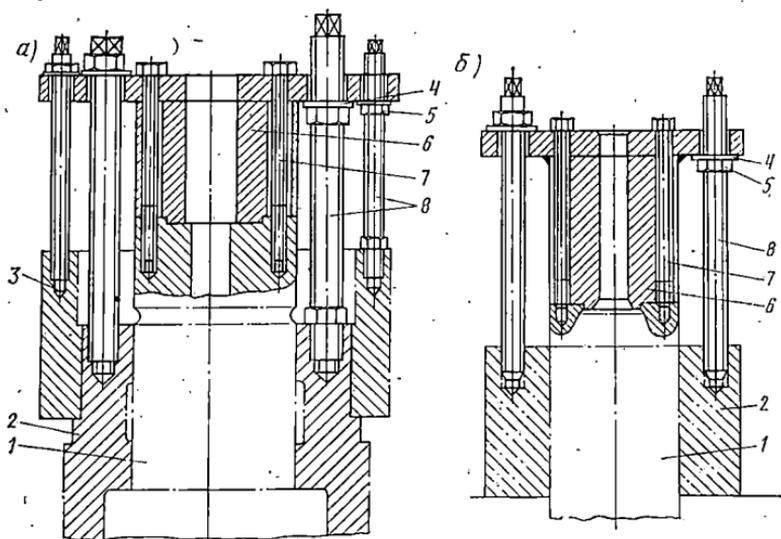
Приспособления для запрессовки и снятия втулки пяты
